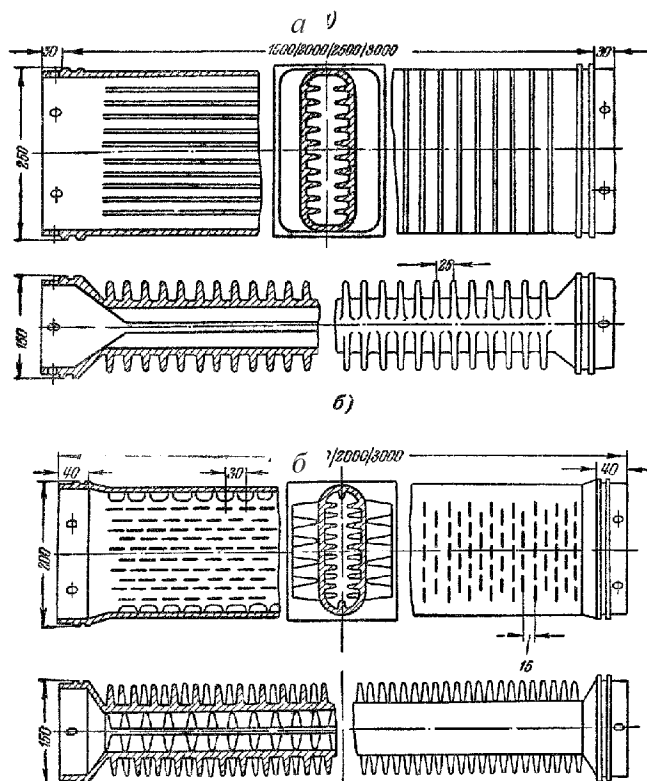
Конструкция элементов чугунных воздухоподогревателей:
